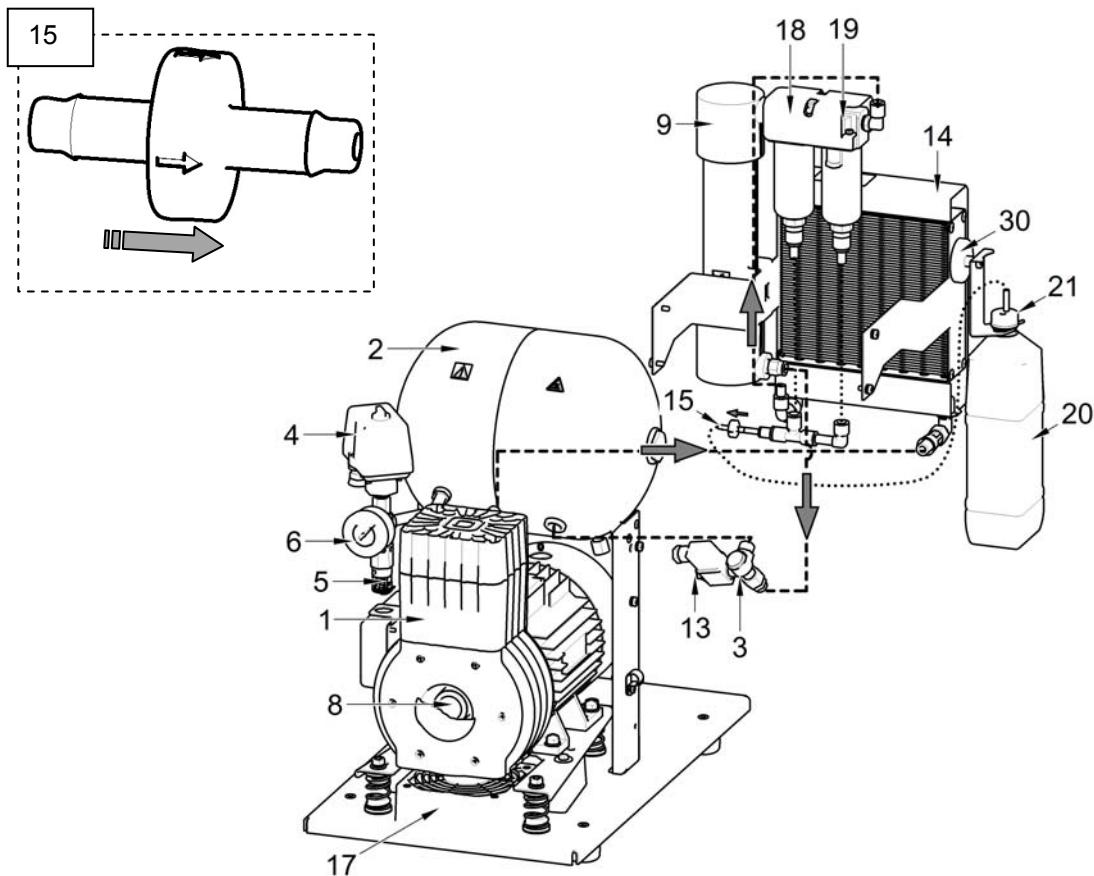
Компрессор DK50-10 Z/M с осушителем воздуха
